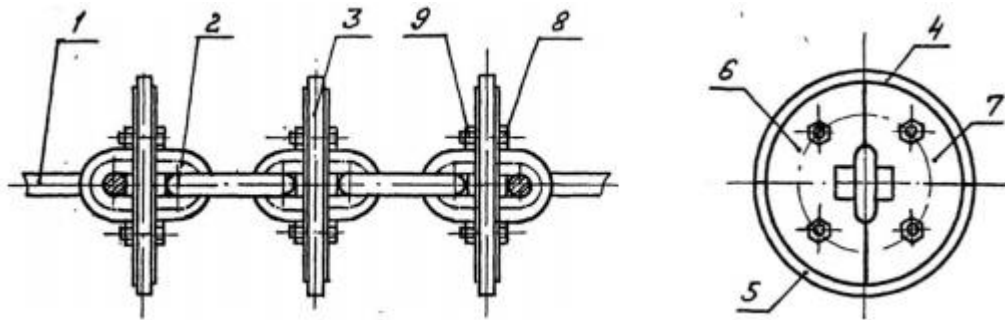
Конструктивна схема трубчатого скребкового конвеєра
